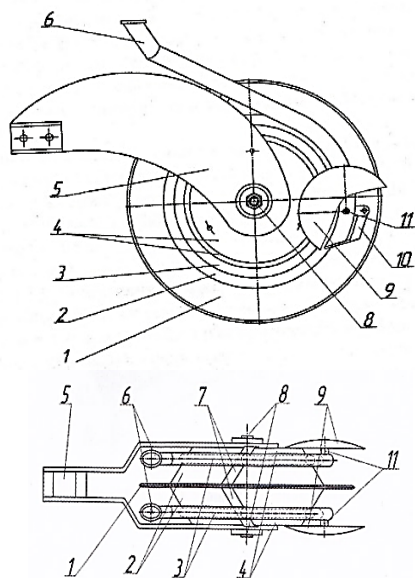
Комбинированный однодисковый сошник с двухсторонними ребрами и сферическими дисковыми загортачами для узкорядного посева: *а* – вид сбоку; *б* – вид сверху; *1* – плоский диск; *2, 4* – реборды; *3* – бороздкообразователи; *5* – корпус; *6* – семянаправители; *7* – чистики; *8* – ось; *9* – сферические диски; *10* – клапан; *11* – оси
